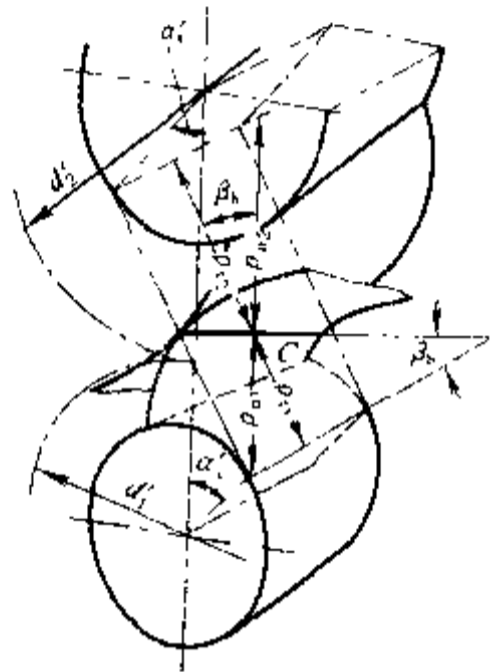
斜齿圆柱齿轮传动节点的曲率半径
